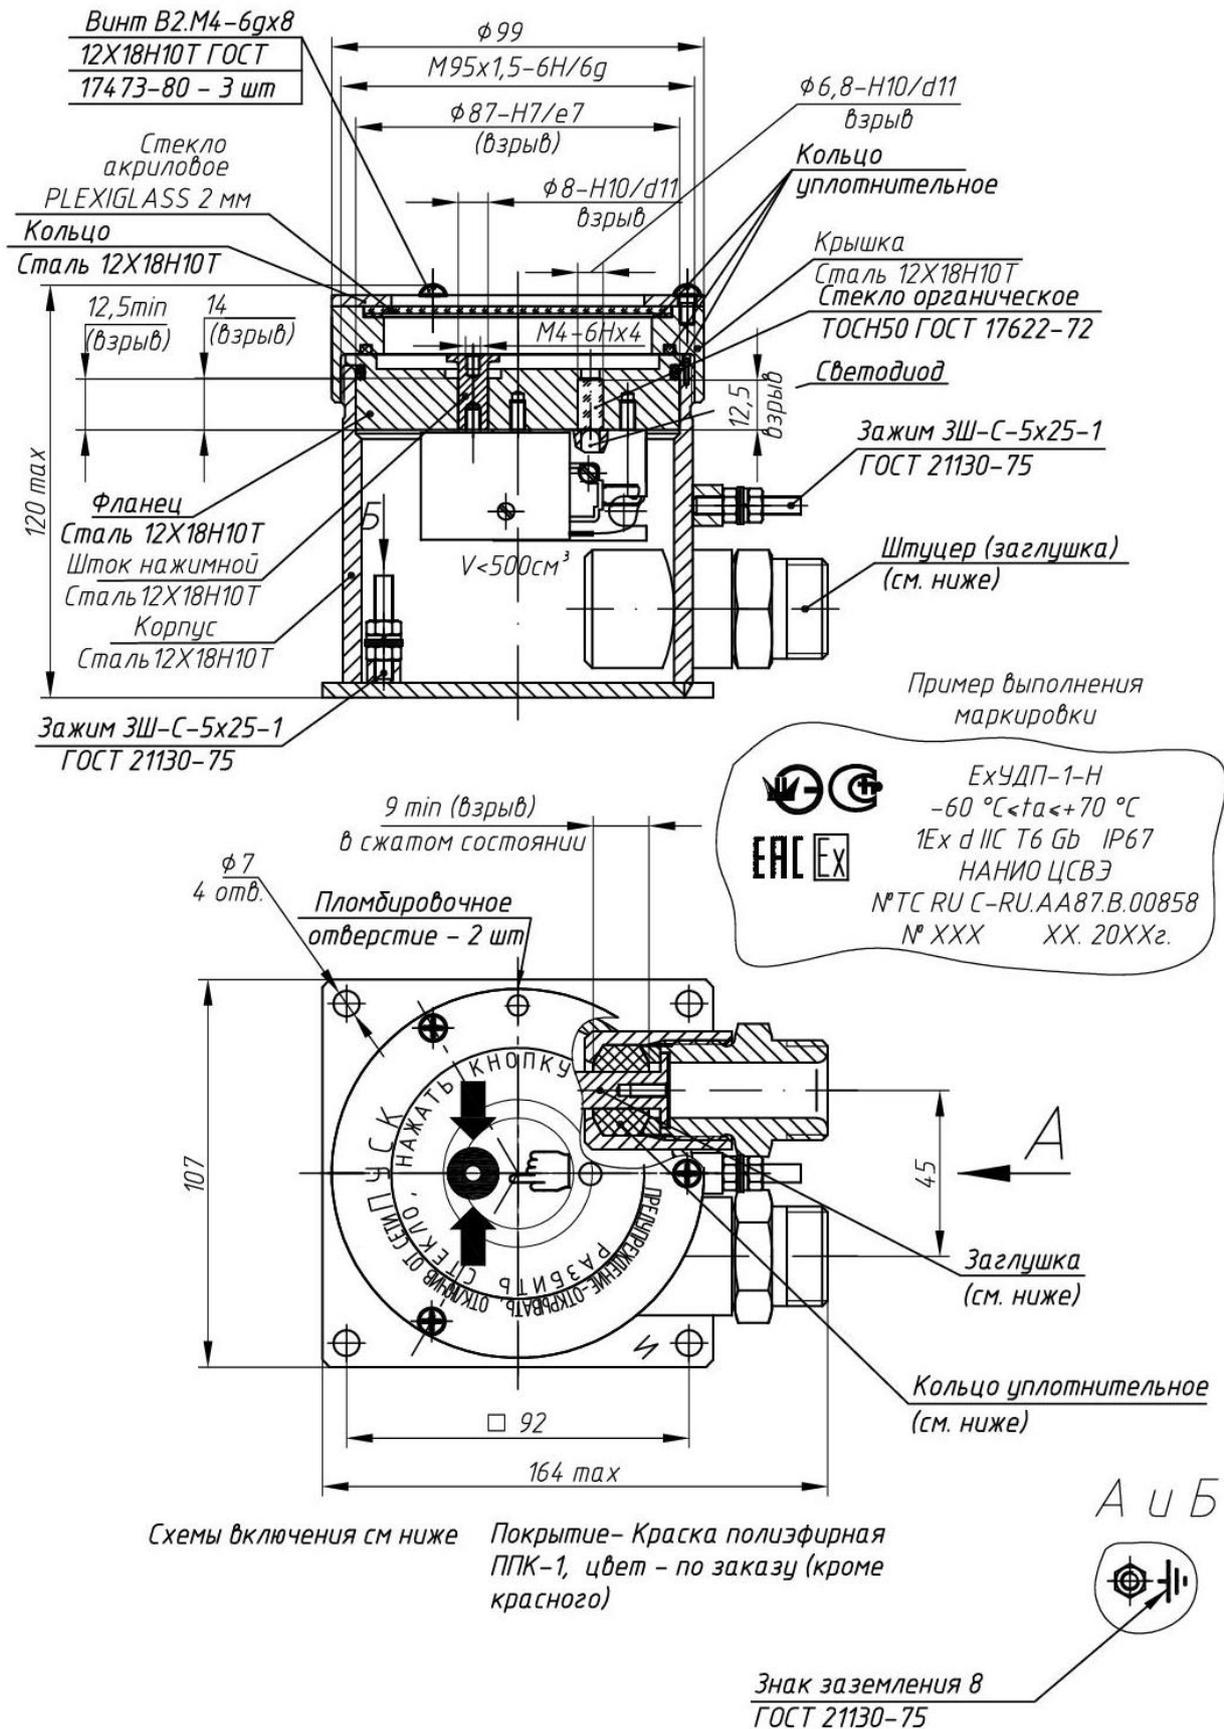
Габаритный чертёж взрывозащищённых устройств дистанционного пуска ExUDP-1 и ExUDP2 в корпусе из нержавеющей стали, совмещённый с чертежом взрывозащиты. Монтаж кабеля диаметром от 8 до 18 мм
